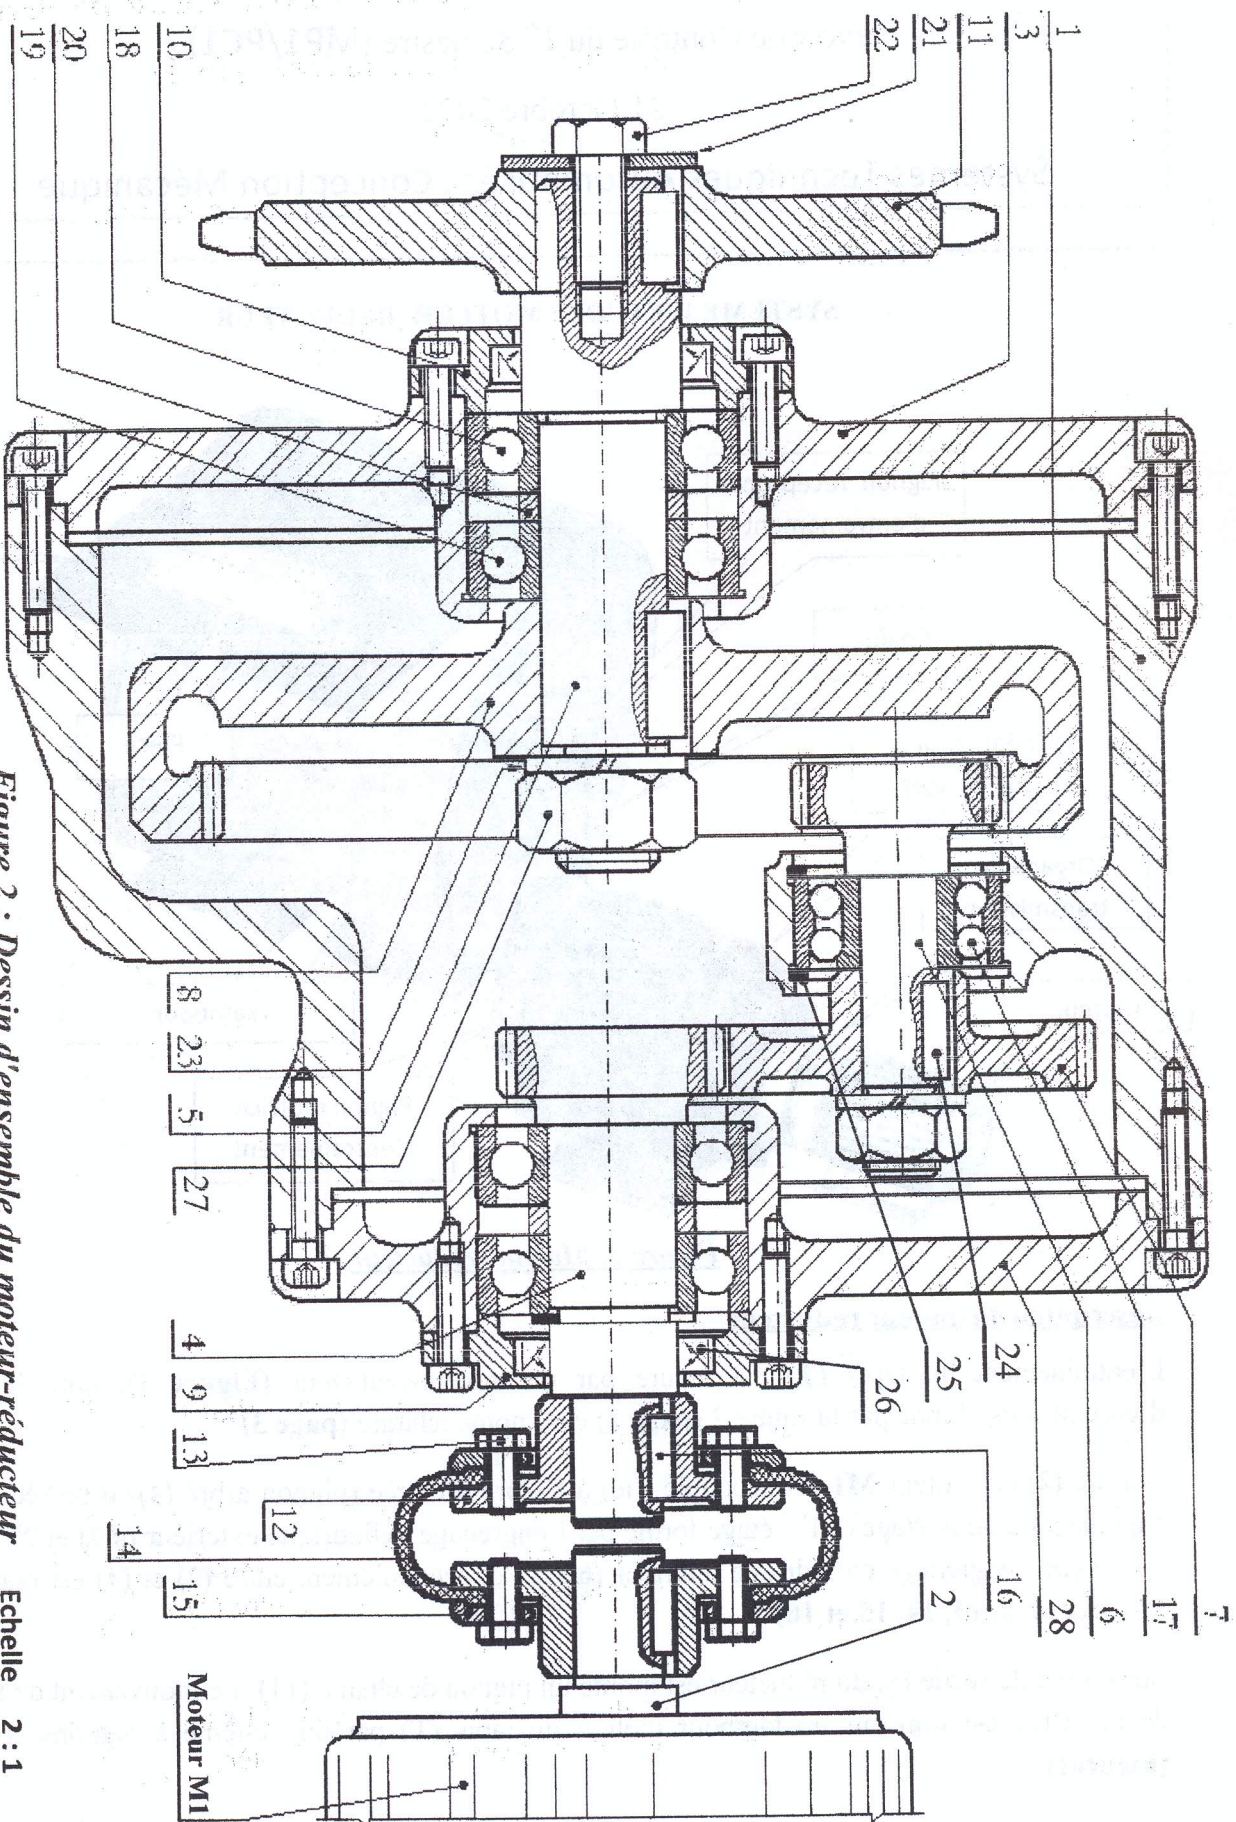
Dessin d'ensemble du moteur-réducteur Echelle 2 : 1
